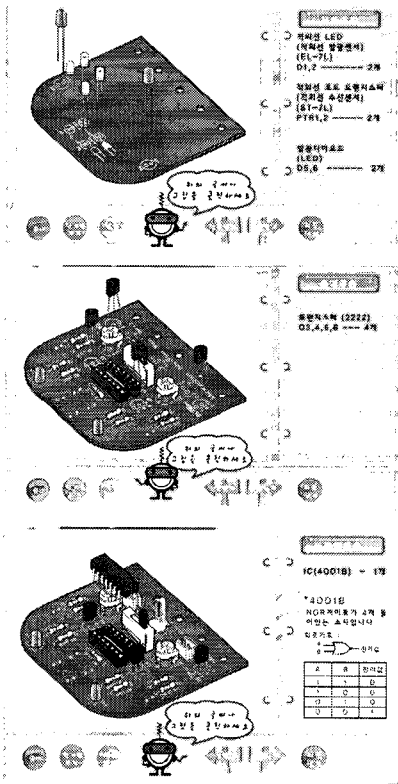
PCB 기판 조립하기의 예(1, 6, 8 단계)
